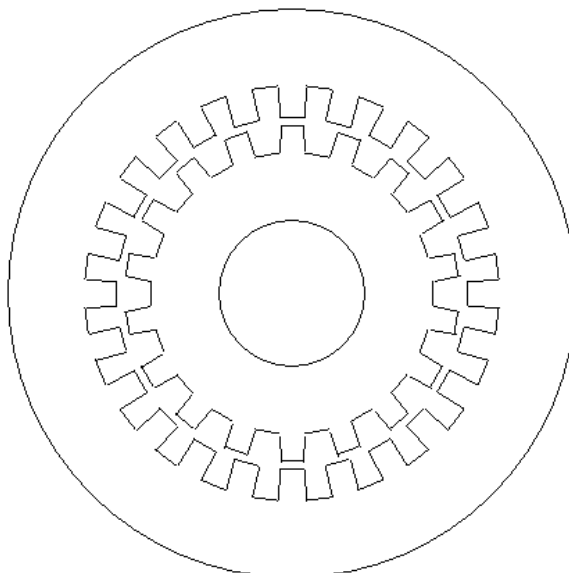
Четырехфазный ВРД конструкции 24/18
